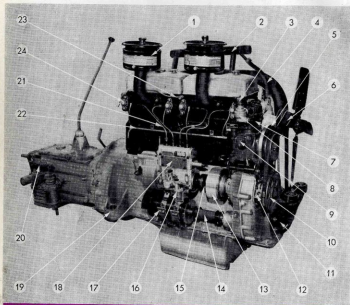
Vue 3/4 droit moteur ZU 4 RB 31.
